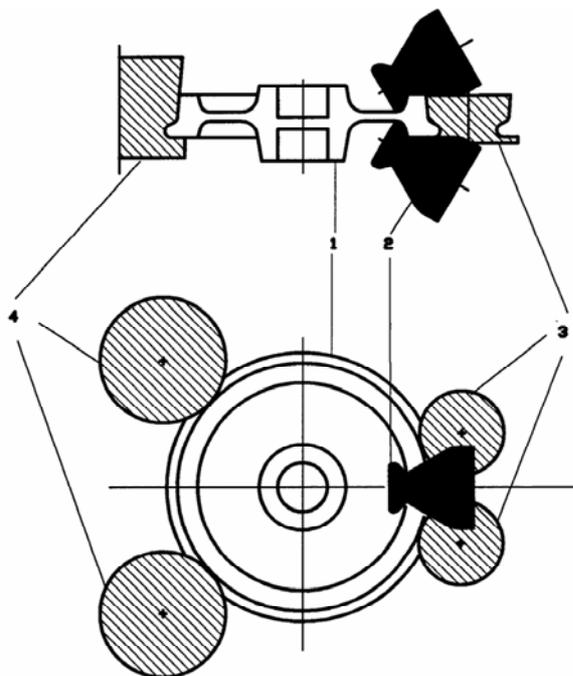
Схема прокатки колеса на колесопрокатном стане:
